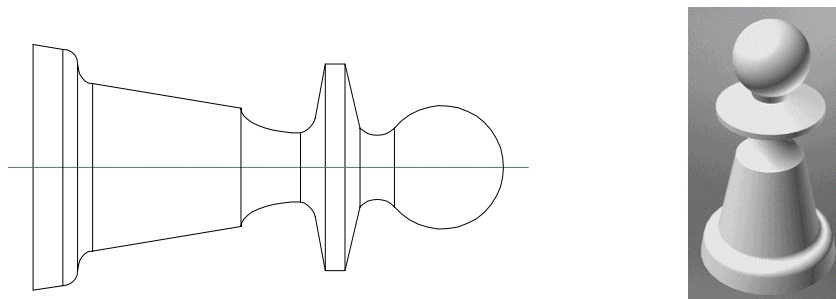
Exemplo de produto: (a) desenho técnico; (b) imagem tridimensional
